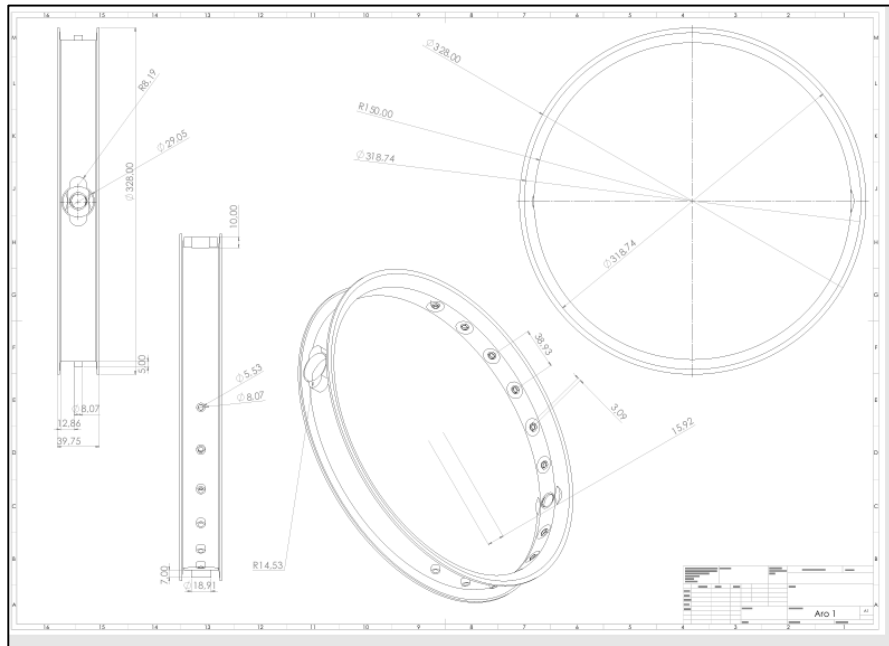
Plano técnico del Aro 1 (Fuente: elaboración propia con SolidWorks)[Aro 1](attachment:Aro 1.pdf)
